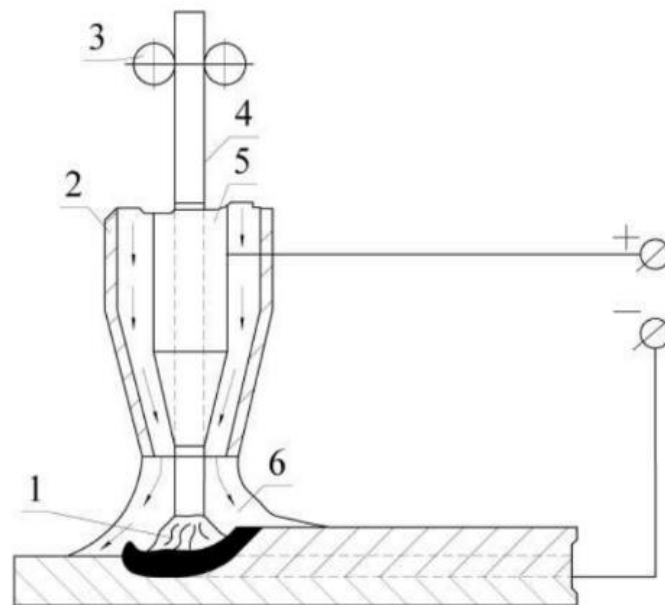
Схема дугового зварювання у вуглекислому газі електродом, що плавиться: 1 – електрична дуга; 2 – газове сопло; 3 – ролики, що подають; 4 – електродний дріт; 5 – струмо-з'єднувальний мундштук; 6 – захисний газ
